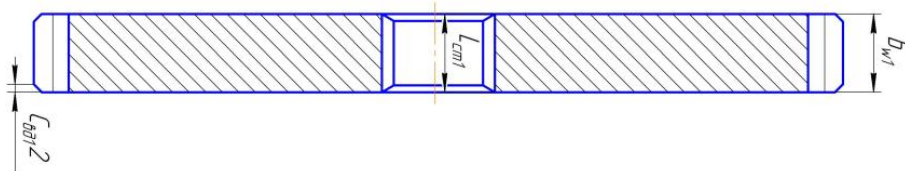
Ведущая шестерня заднего колесного редуктора
